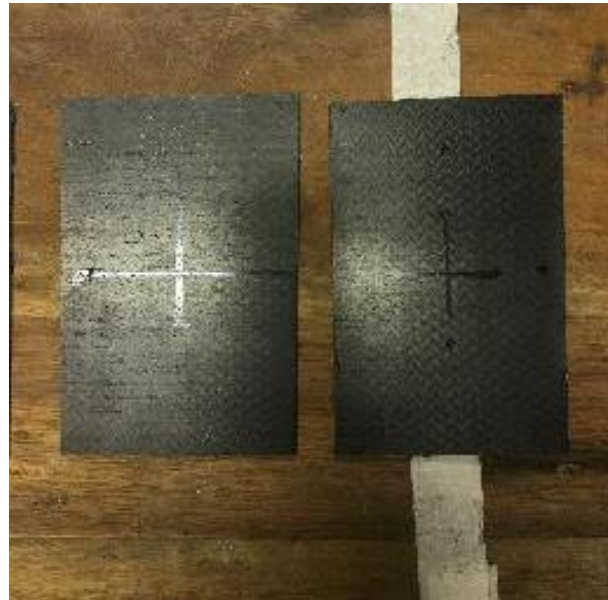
Corpos de prova para ensaios a 90° após o corte com serra manual.
